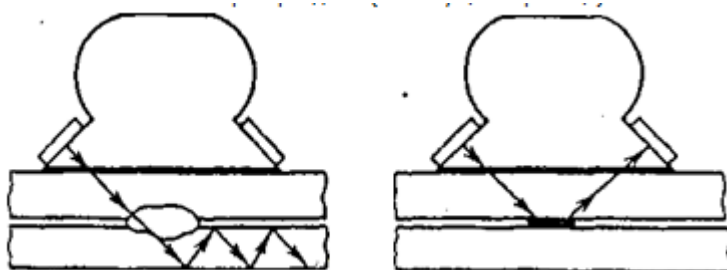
Схема прохождения ультразвука в сварной точке
